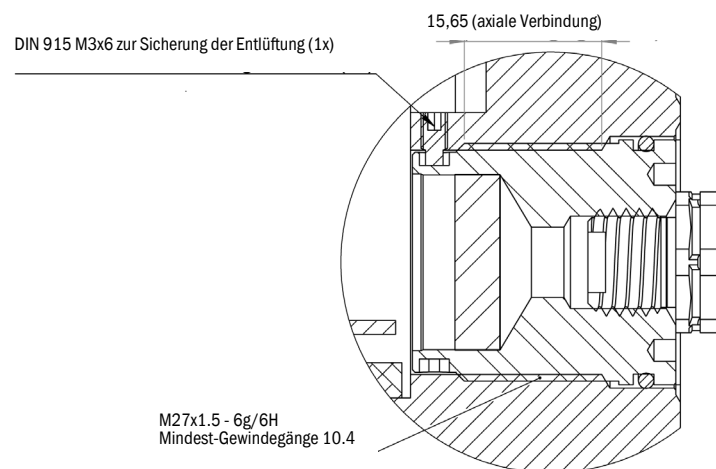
Verschraubter Flammweg zwischen Ex-Entlüfter und Ex-Gehäusekörper
